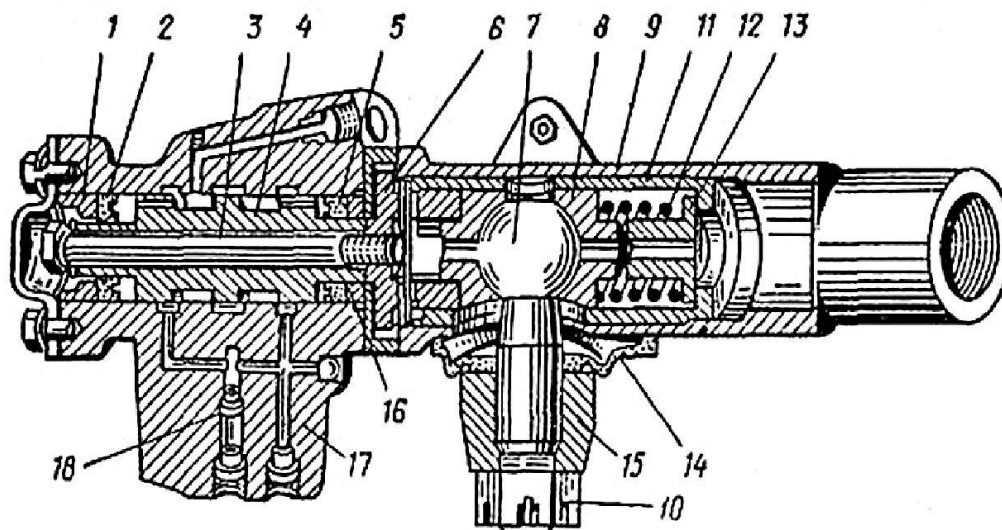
Распределитель усилителя автомобиля ГАЗ 66:
